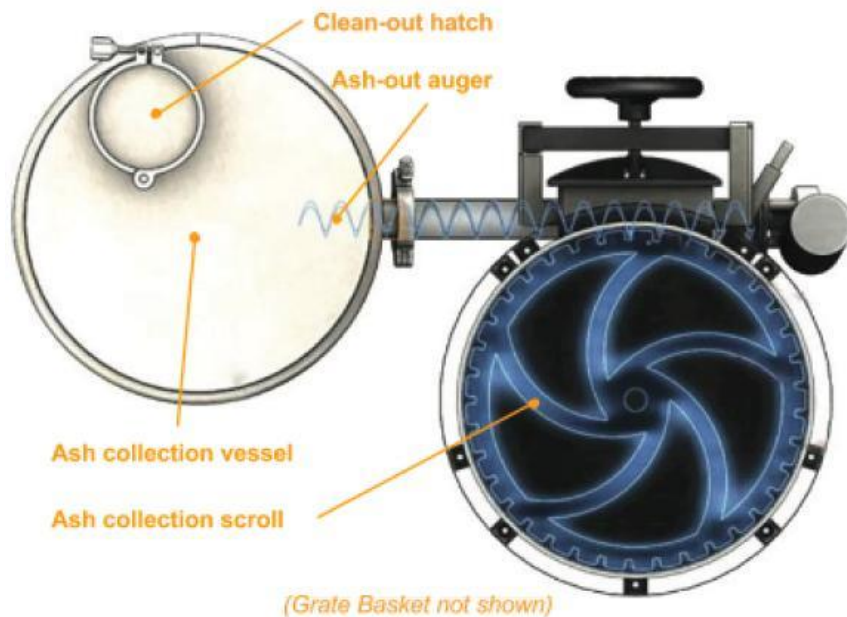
Ascheaustrag – Grundriss [35]
